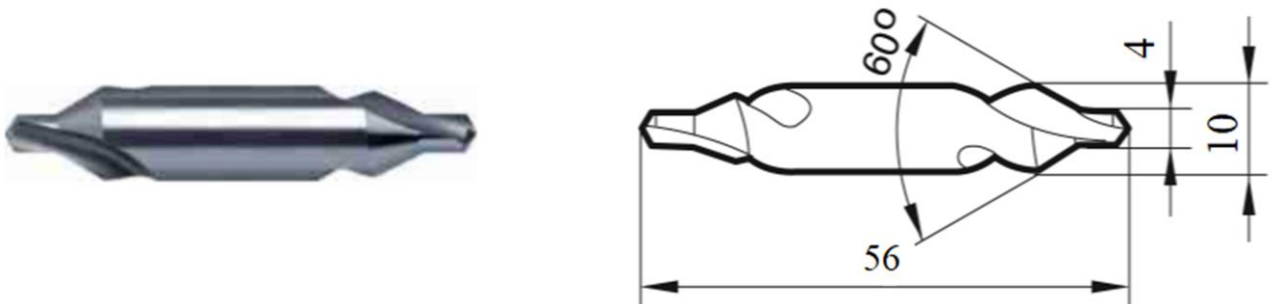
Центрувальне свердло $\text{Ø}4\text{mm}$ 9003810040000.
